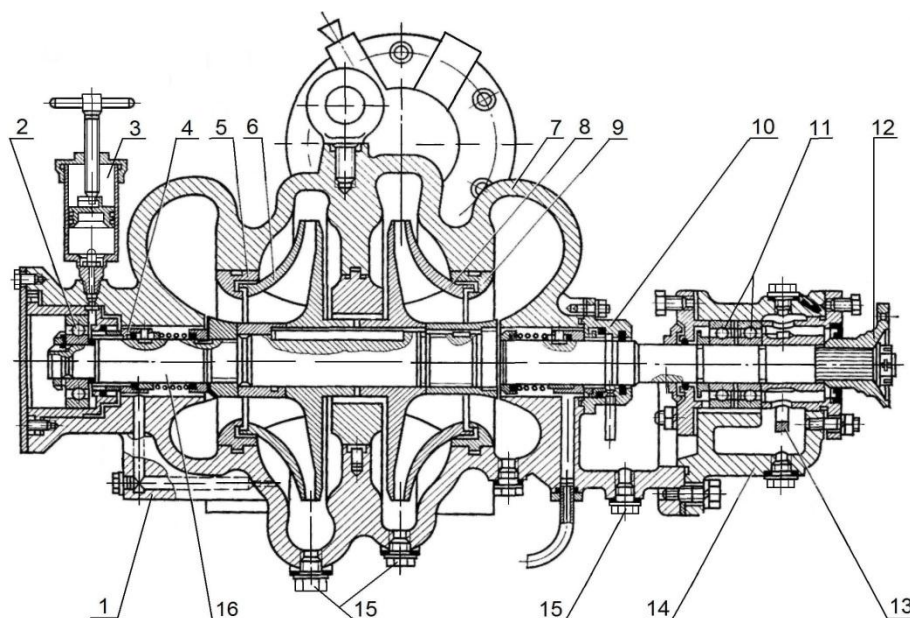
Общее устройство насоса 6НГМ-7х2А: 1 - корпус; 2 - подшипник № 308; 3 - масленка; 4 - уплотнительное кольцо; 5 - уплотнительное кольцо первой ступени; 6 - рабочее колесо первой ступени; 7 - крышка; 8 - рабочее колесо второй ступени; 9 - уплотнительное кольцо второй ступени; 10 - корпус сальника; 11 - подшипник № 46308; 12 - муфта фланца первичного вала раздаточной коробки; 13 - кольцо для смазки; 14 - корпус подшипника; 15 - пробка; 16 - вал насоса
